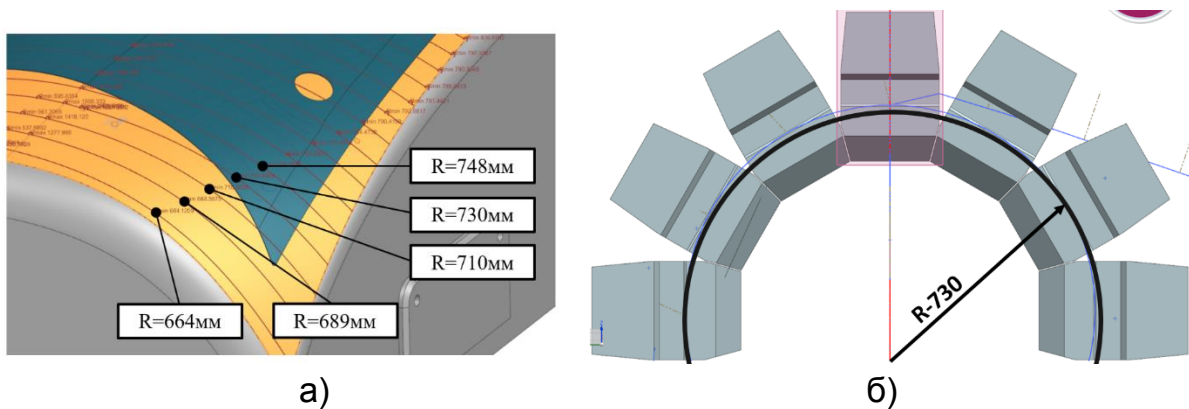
Радиус изгиба в носовой части обшивки (а), минимальный радиус искривления губок пресса (б)
